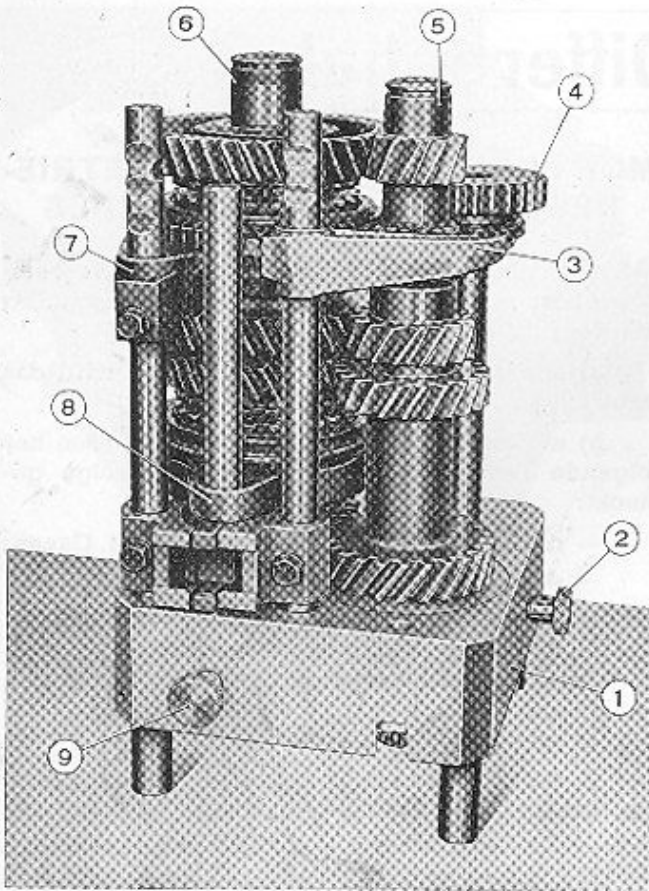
Vorläufige Montage des Getriebes auf dem Werkzeug A. 70105.
